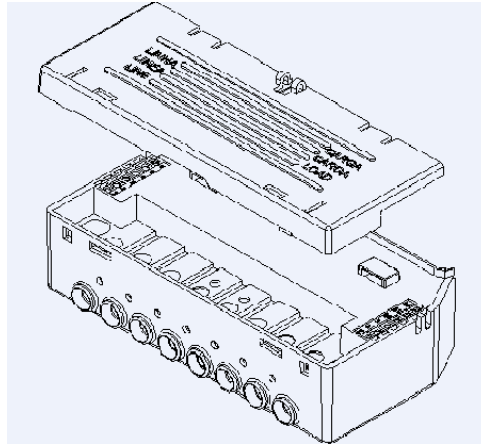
Detalhe da tampa do bloco de terminais do ELO 2113.
